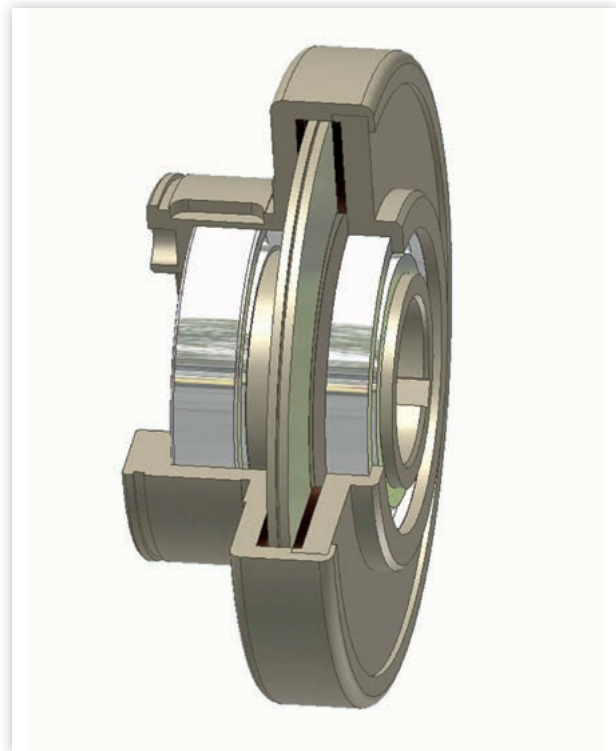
Budowa sprzęgła VHT. 1 – korpus zewnętrzny sprzęgła, 2 – wirnik, 3 – okładzina ciarna, 4 – łożyska, 5 – koło zębate, 6 – wpust, X – luz na średnicy, Y – luz pomiędzy membraną a korpusem zewnętrznym, A – otwór doprowadzający olej.
